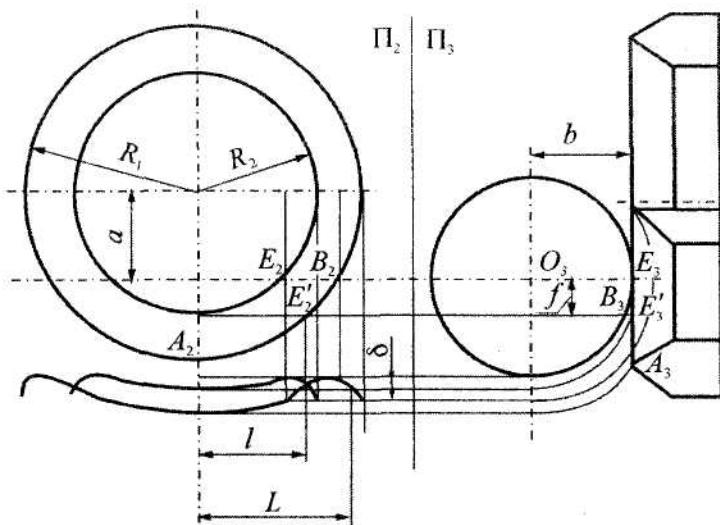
Схема формоутворення круглої циліндричної поверхні торцевою фрезою, зуби якої розташовані на різних діаметрах
